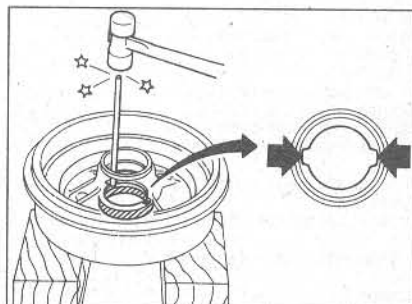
Выбивание наружных колец подшипника задней ступицы (Глава 13)
